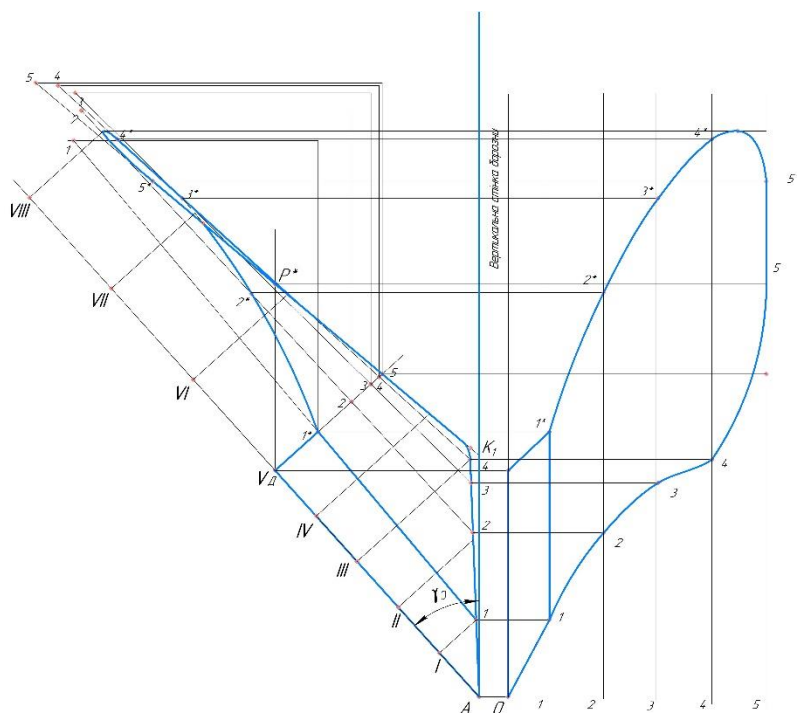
Побудова горизонтальної і бокової проекцій робочої циліндроїдальної поверхні корпусу
